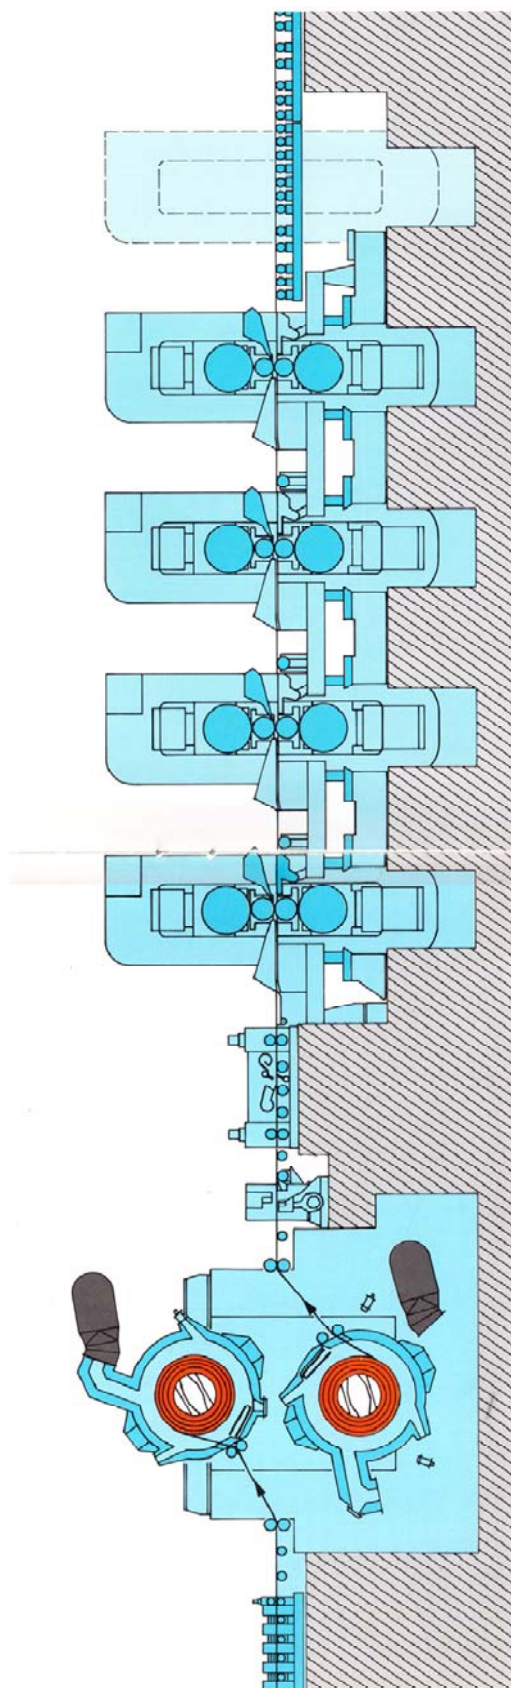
Моталки CremonaВoхи чистовой стан агрегата
